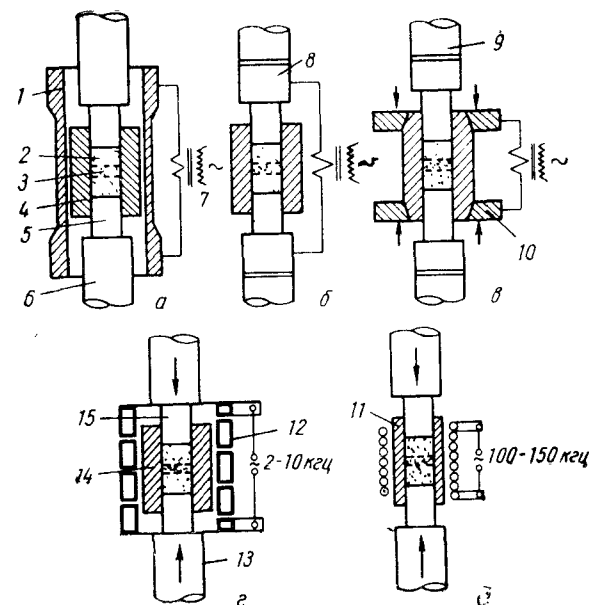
Установки для горячего прессования с различными способами нагрева:
